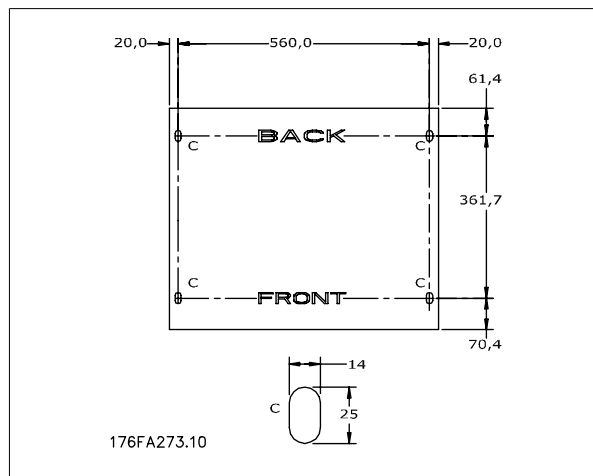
Bohrschablone für Befestigungslöcher im Boden.
